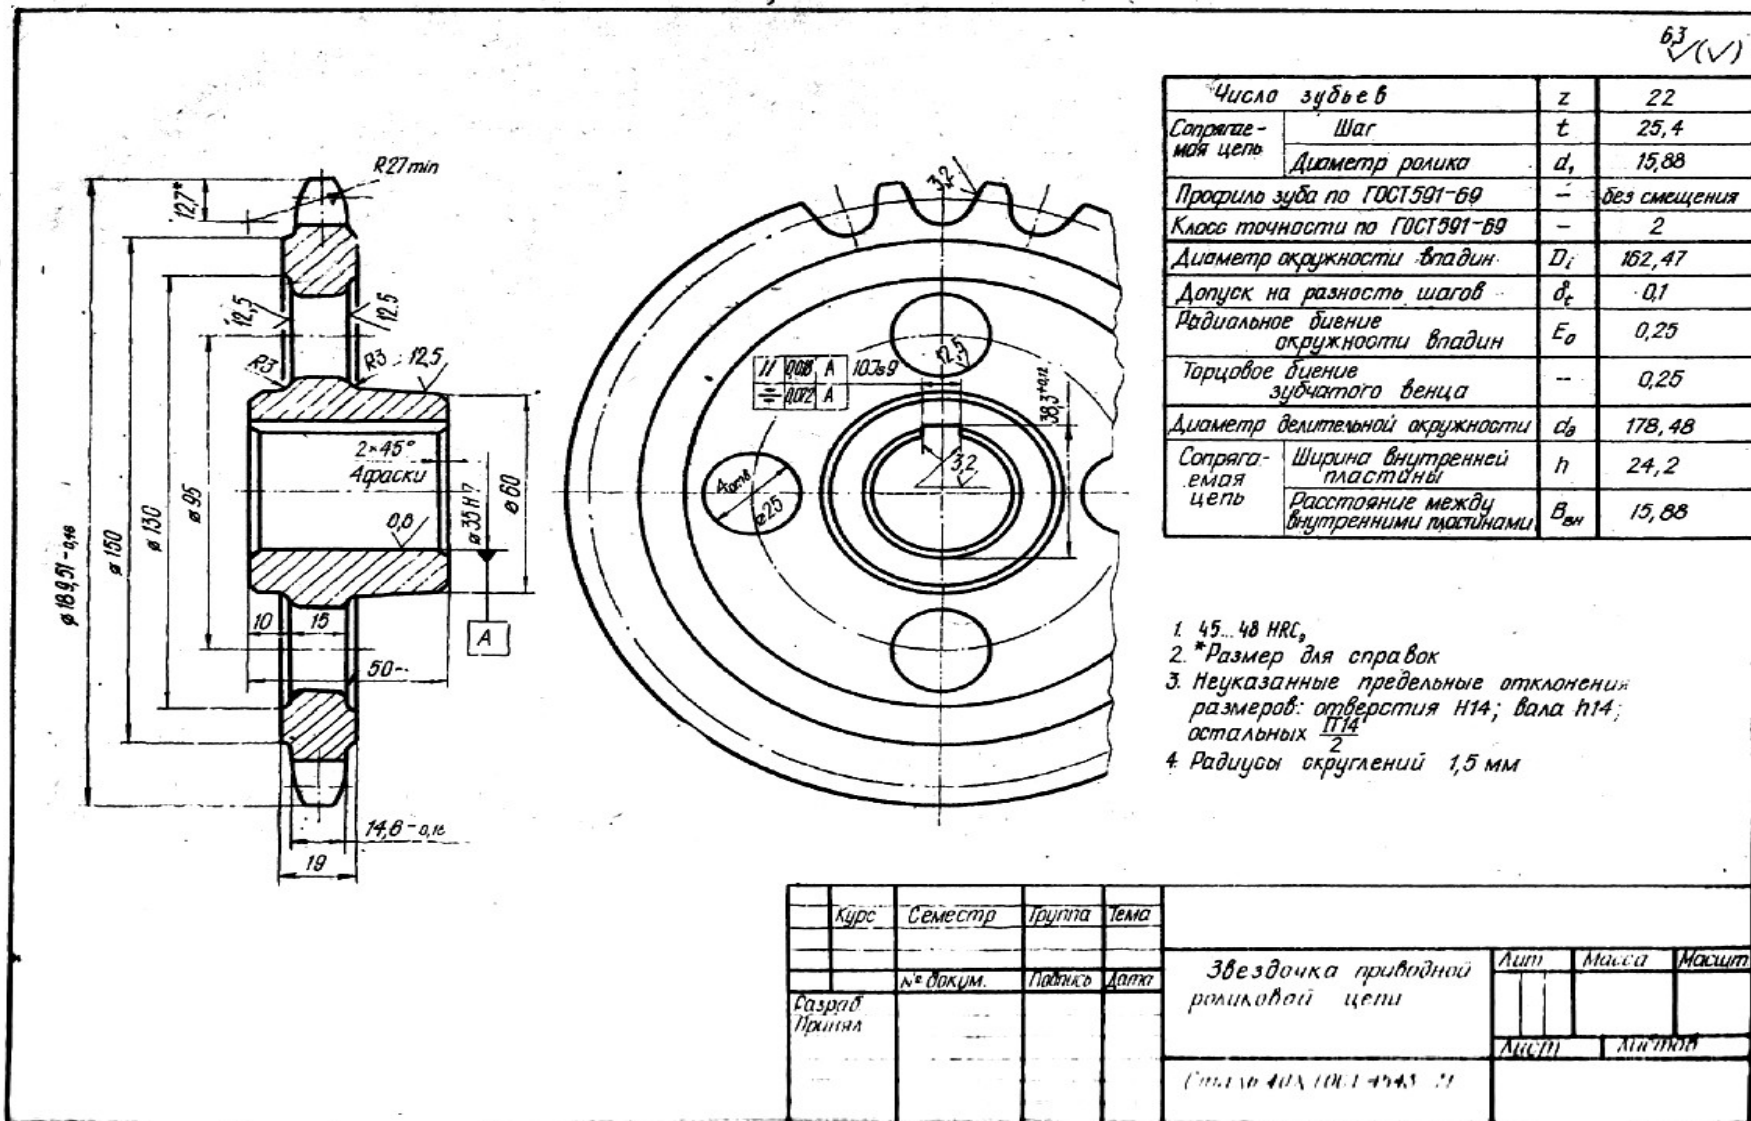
Робоче креслення зірочки ланцюгової передачі
